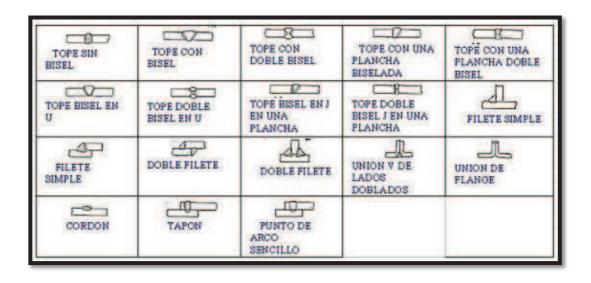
Imagen de los tipos de soldadura
